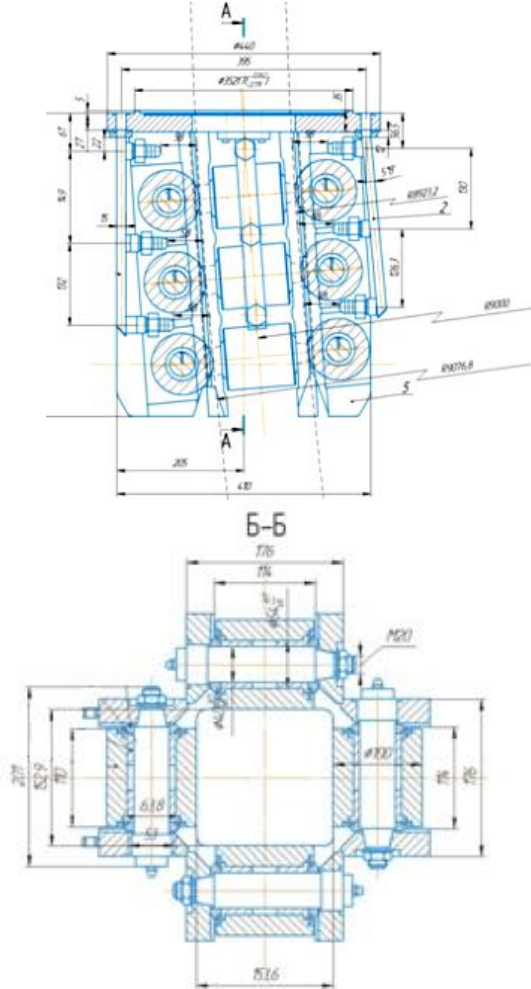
Общий вид и схема расположения координат осей отверстий под ролики ЗВО
